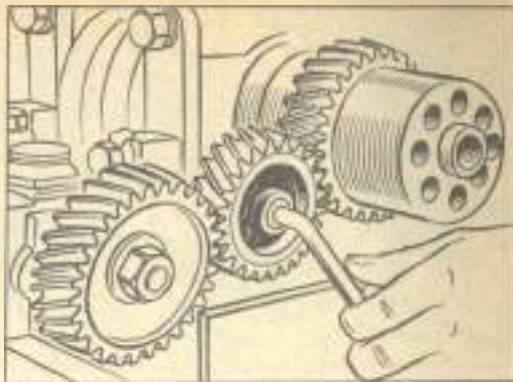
Выворачивание внутреннего болта из вала промежуточной шестерни привода масляного насоса
